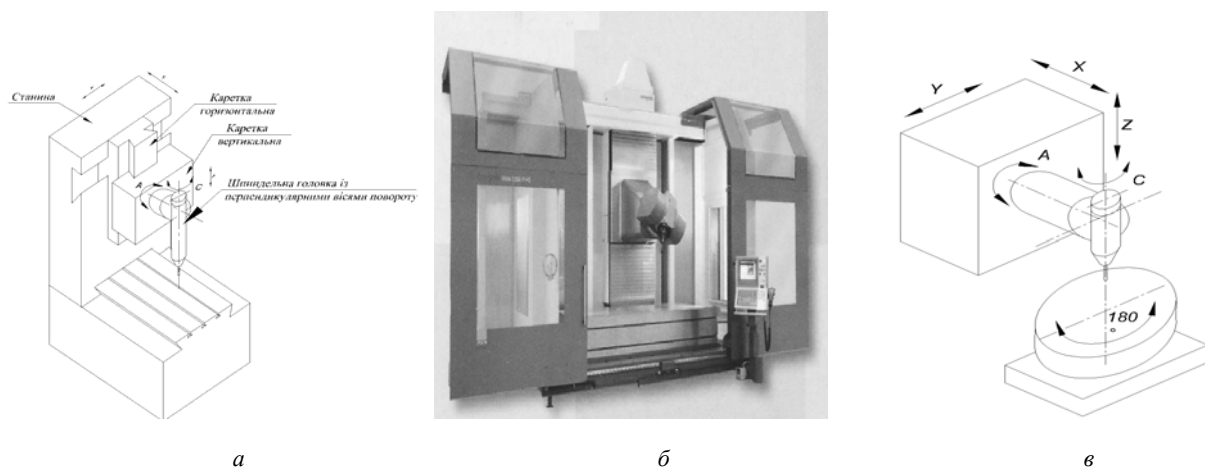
Безконсольний вертикально-фрезерний верстат із поворотною головкою та перпендикулярними осями повороту головки і шпинделя: а) конструктивна схема, б) фото, в) принципова схема
